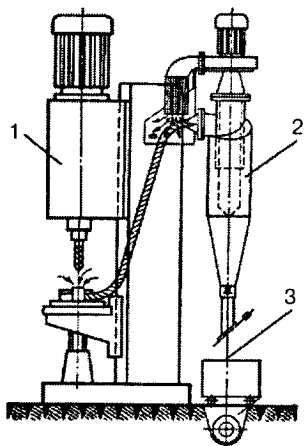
Схема оснащення вертикально-свердлильних верстатів пристроями видалення стружки й пилу:
